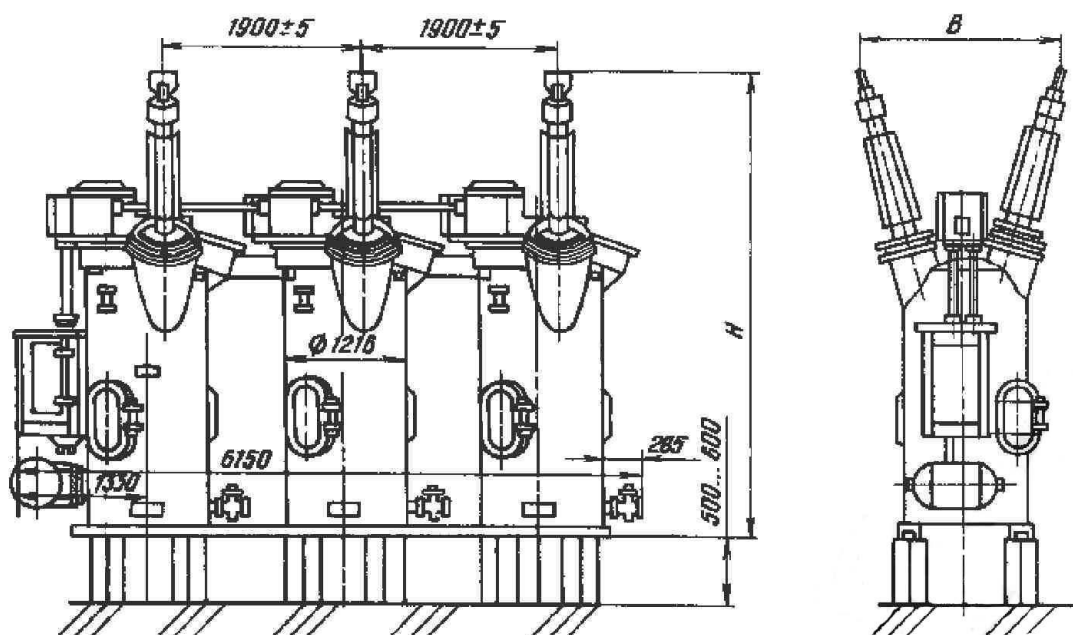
Общий вид, габаритные размеры выключателя У-110
